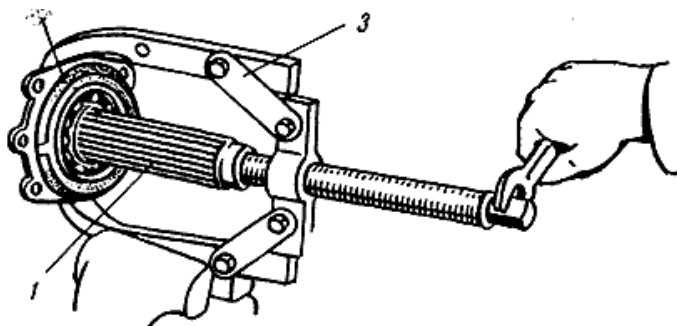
Выпрессовка первичного вала: 1- первичный вал; 2- стакан;
